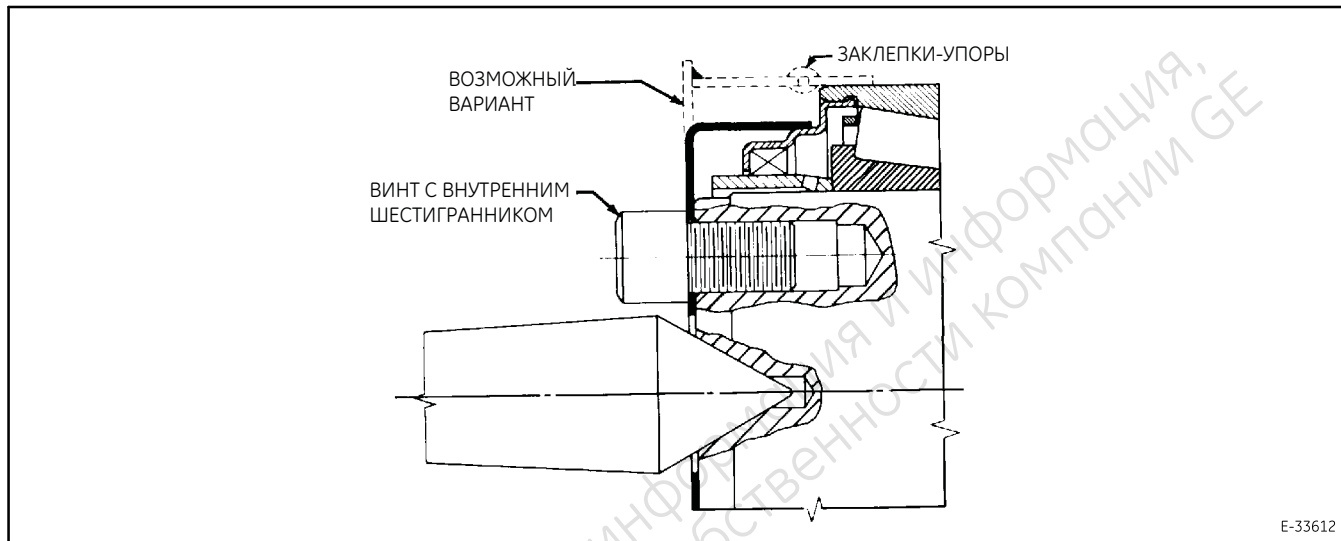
Приспособление для защиты подшипника при обточке колеса.
